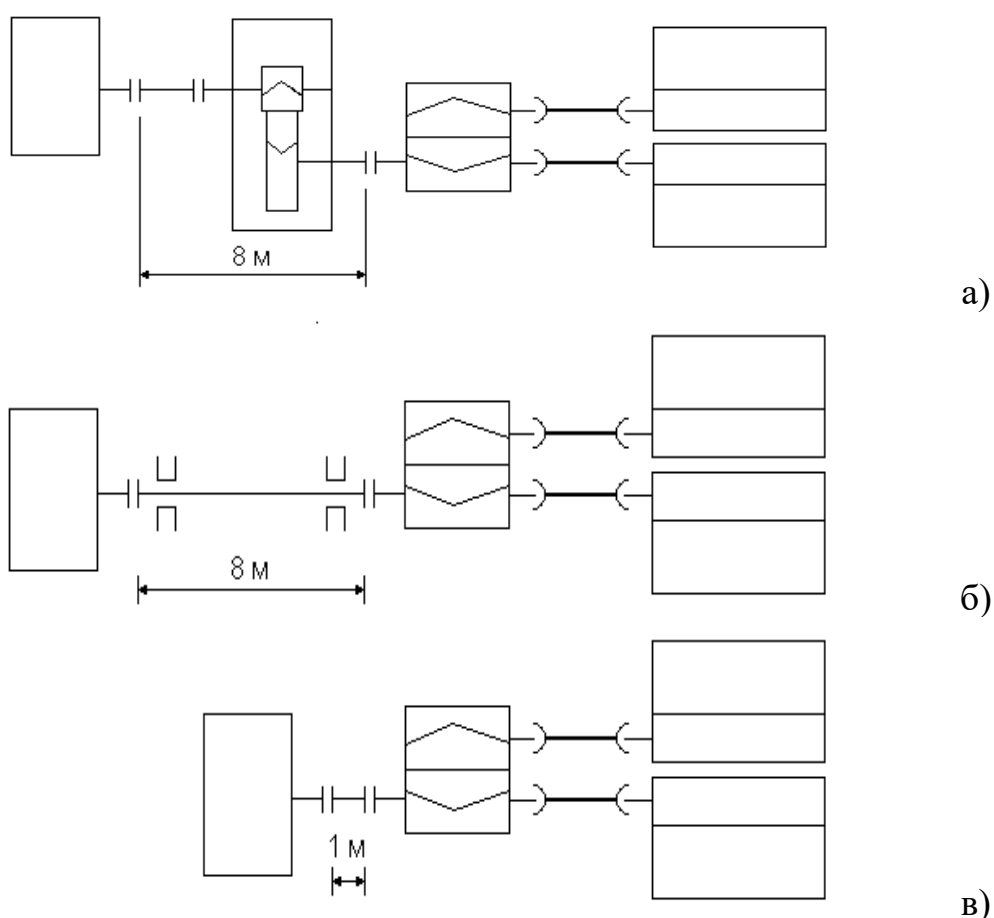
Схеми лінії приводу прокатних клітей чистової групи: а - існуюча схема з редуктором; б - заміна редуктора проміжним валом, довжиною 8 м; в - установка електродвигуна безпосередньо на місце редуктора; проміжний вал довжиною 1 м.
